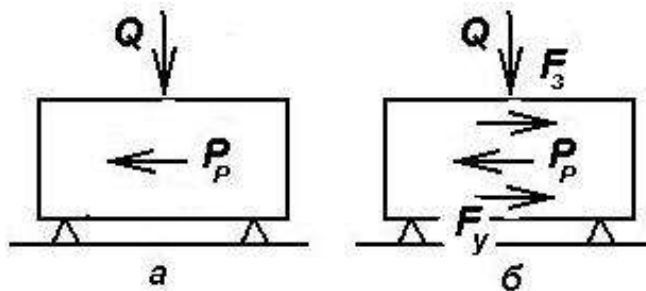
Схема впливу зусиль при обробці (а) та розрахункова схема (б) при зсуві заготовки на опорах
